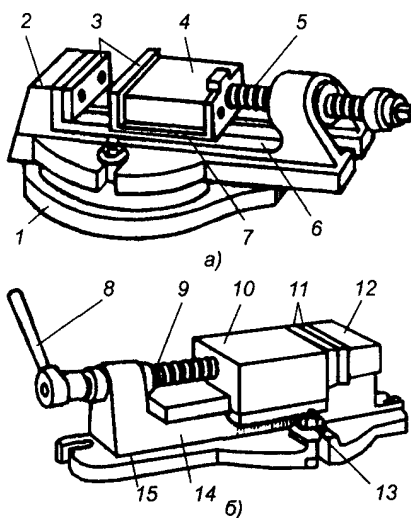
Машинные поворотные (*a*) и неповоротные (*б*) тиски: 1, 14 — основания; 2 — неподвижные губки; 3 — планка; 4 — подвижные губки; 5 — ходовой винт; 6 — направляющие; 7 — прижим; 8 — рукоятка; 9 — винт; 10, 12 — губки; 11 — прижимные планки; 13 — болт; 15 — упор
